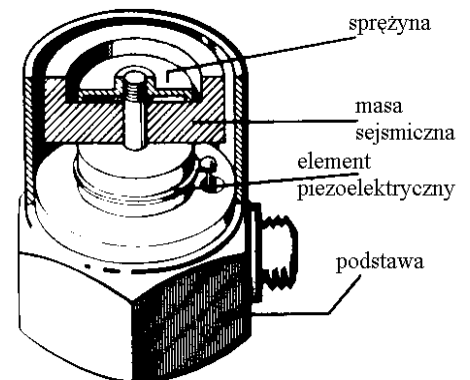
Przekrój przez konstrukcję DeltaShear®.
